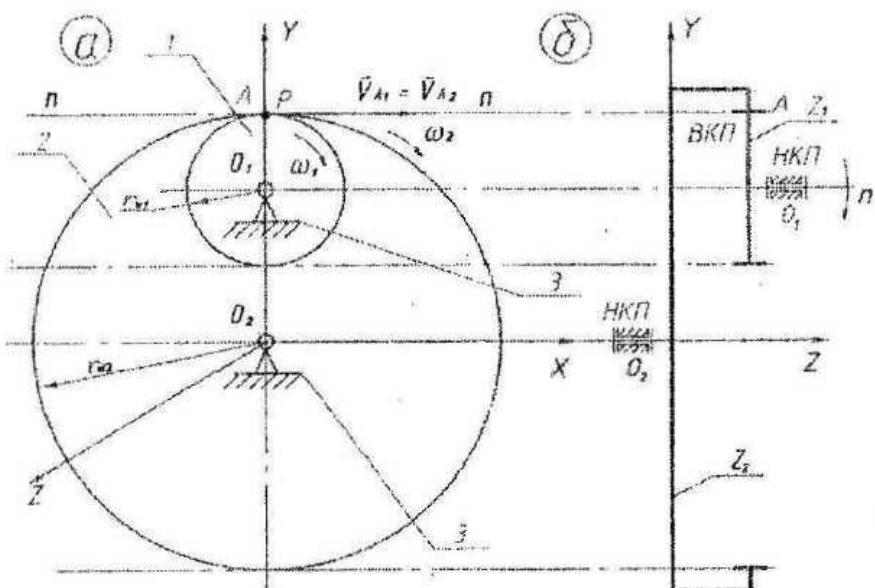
Кинематическая схема одноступенчатой зубчатой передачи с внутренним зацеплением:
